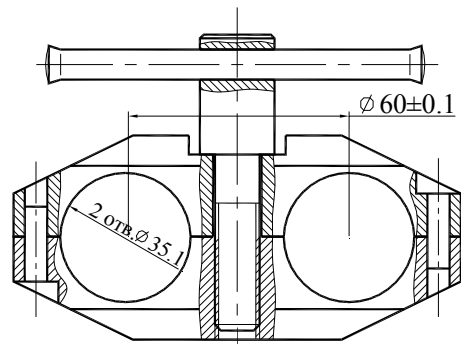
Приспособление для установки клапана черт.ОК-0112СБ
